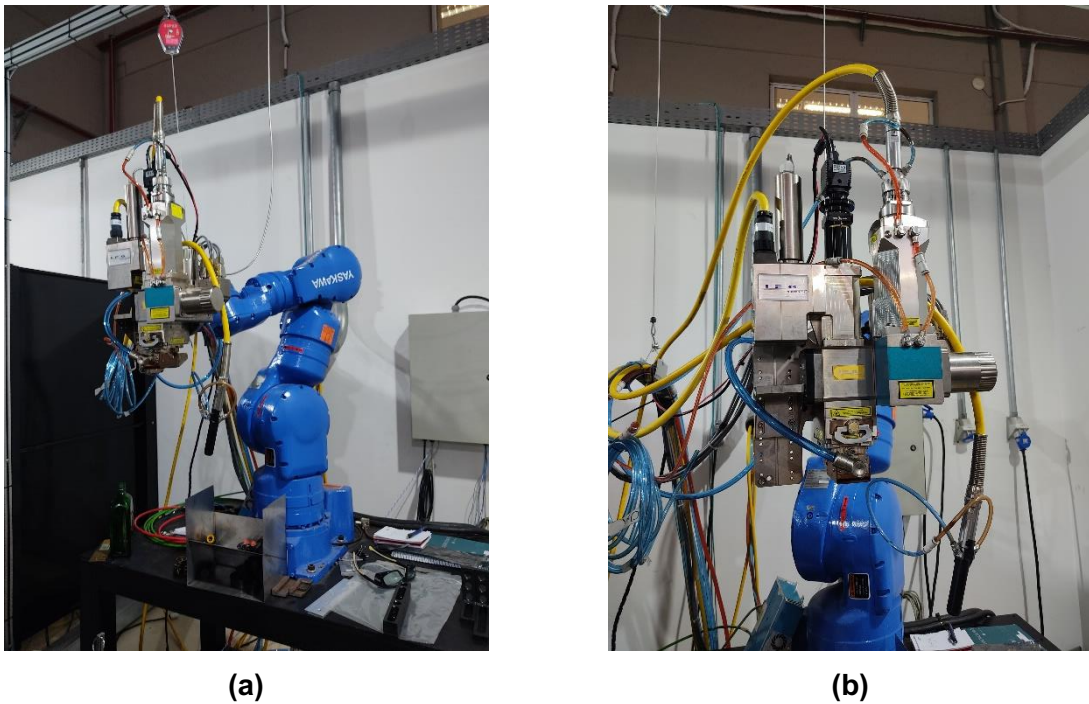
Conjunto robô soldador: (a) Motoman YR-S1A020F; (b) cabeçote IPG 3DM3R.
